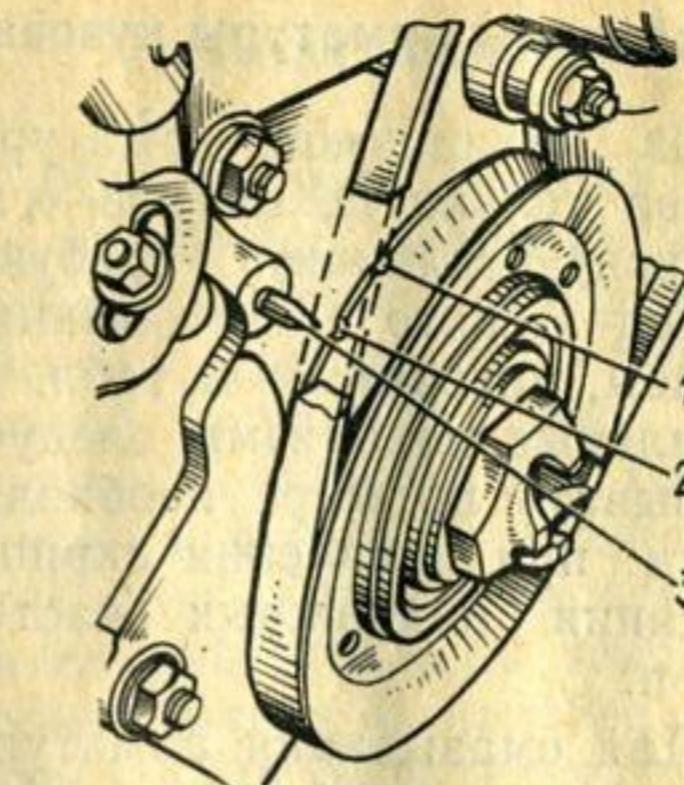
Установочные метки на ободе ведущего шкива коленчатого вала:
